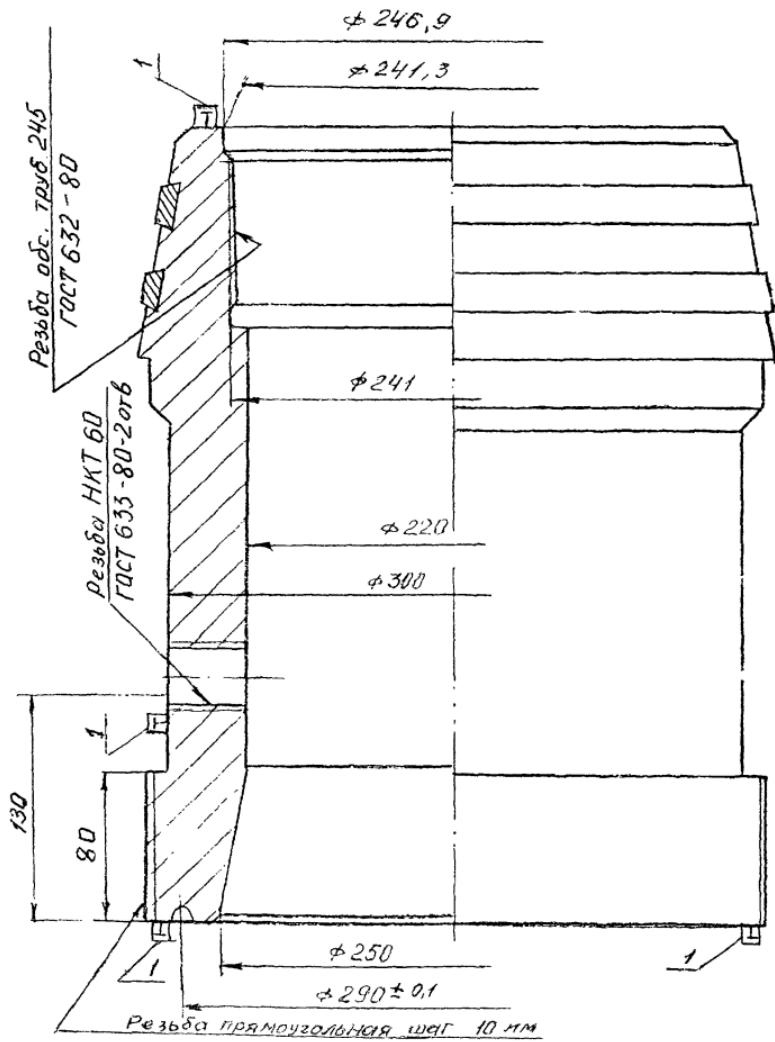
Схема контроля конуса 9" КГ 350-20СБ
